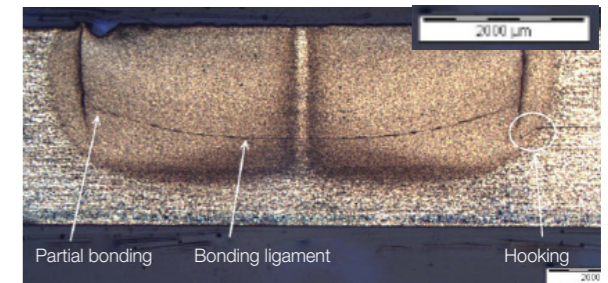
Profil typique d'une soudure dans une pièce en aluminium EN AW-6082-T6 (épaisseur de la tôle: 2 mm)
